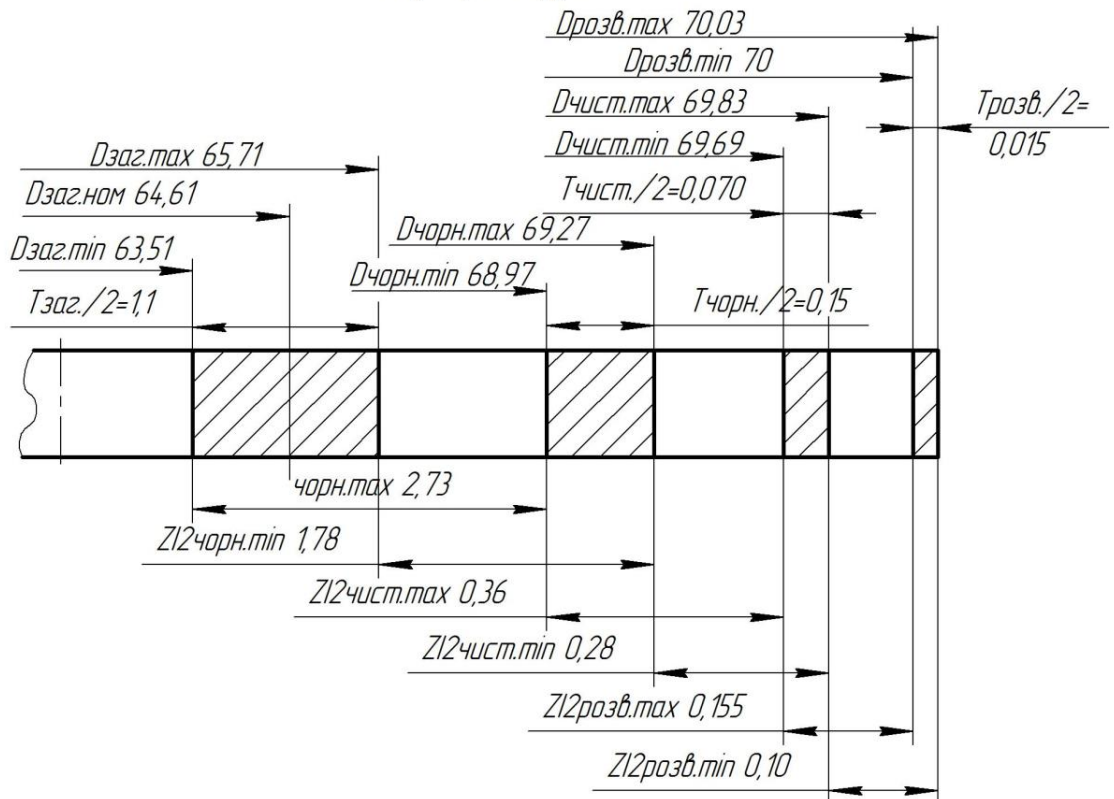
Схема розміщення припусків та допусків на обробку отвору А 70H7(+0,030)
